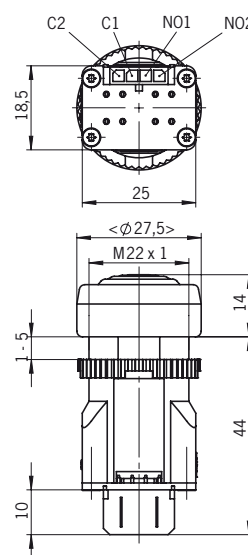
Размерный чертёж выключателя подтверждения ZXE
